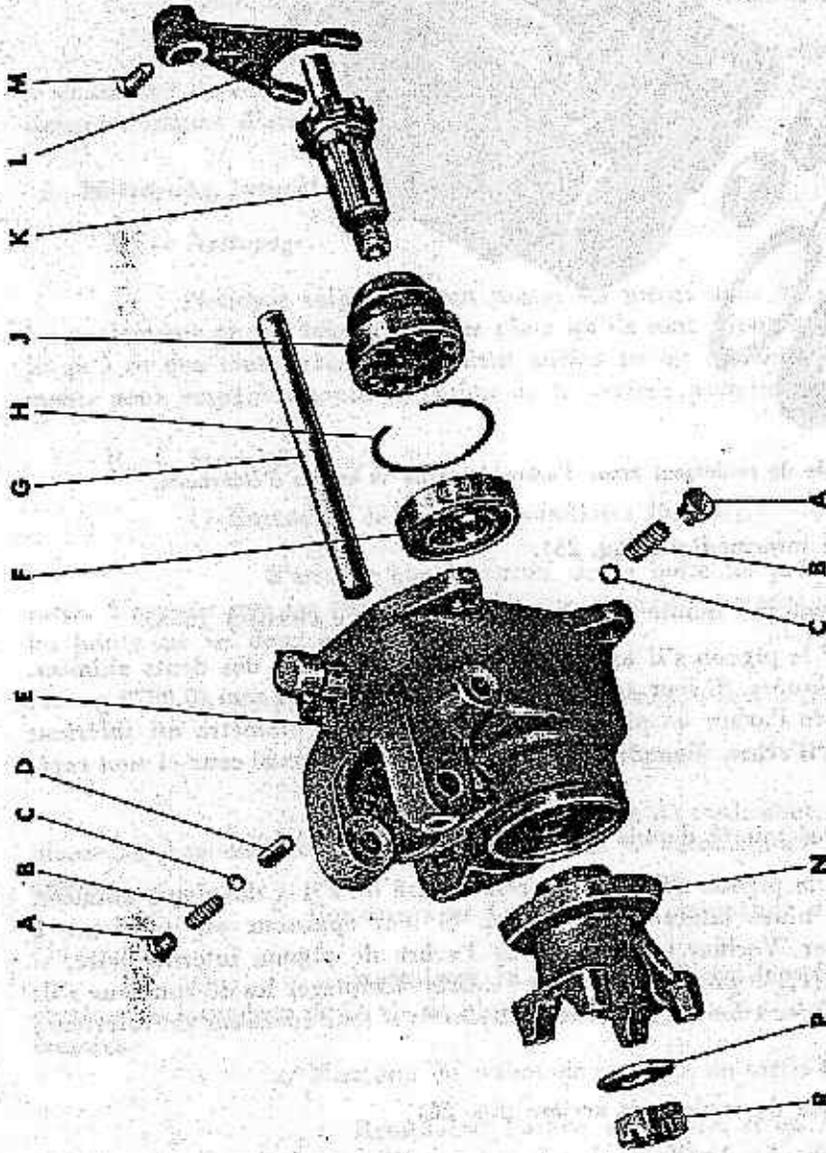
Couvertre de roulement avant d'arbre de sortie. Vue éclatée.
